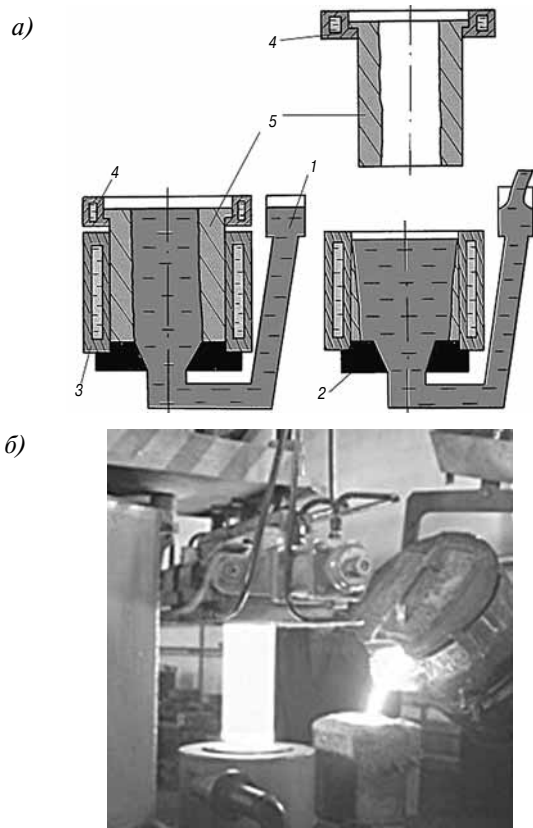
Принципиальная схема (а) и процесс непрерывно-циклического литья полых заготовок без стержня (б): 1 — металлопровод; 2 — соединительный стакан; 3 — стационарная часть кристаллизатора; 4 — подвижная часть кристаллизатора (захваты); 5 — отливка
